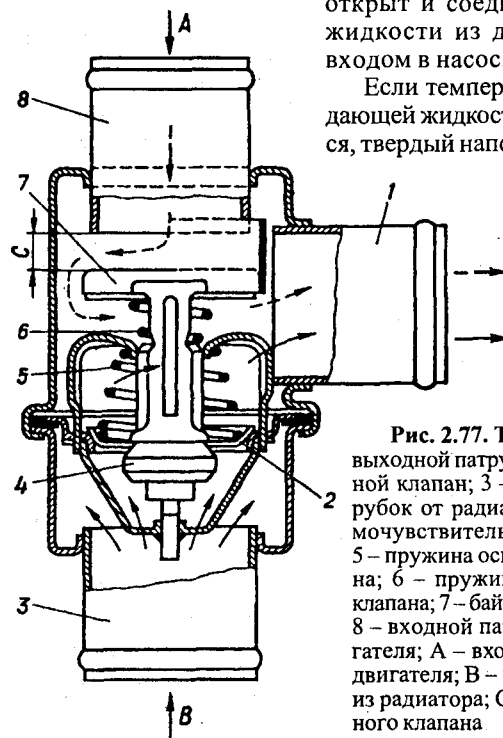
Термостат: 1 – выходной патрубок; 2 – основной клапан; 3 – входной патрубок от радиатора; 4 – термомчувствительный элемент; 5 – пружина основного клапана; 6 – пружина байпасного клапана; 7 – байпасный клапан; 8 – входной патрубок от двигателя; А – вход жидкости из двигателя; В – вход жидкости из радиатора; С – ход байпасного клапана
